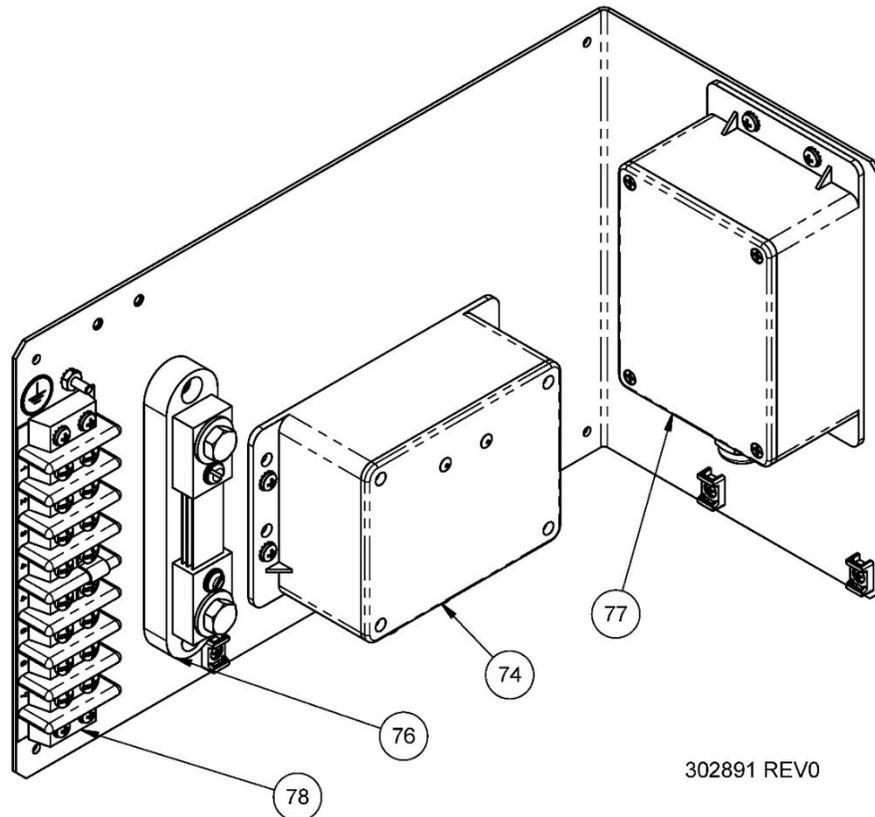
Piezas de ensamblaje de componentes electrónicos
